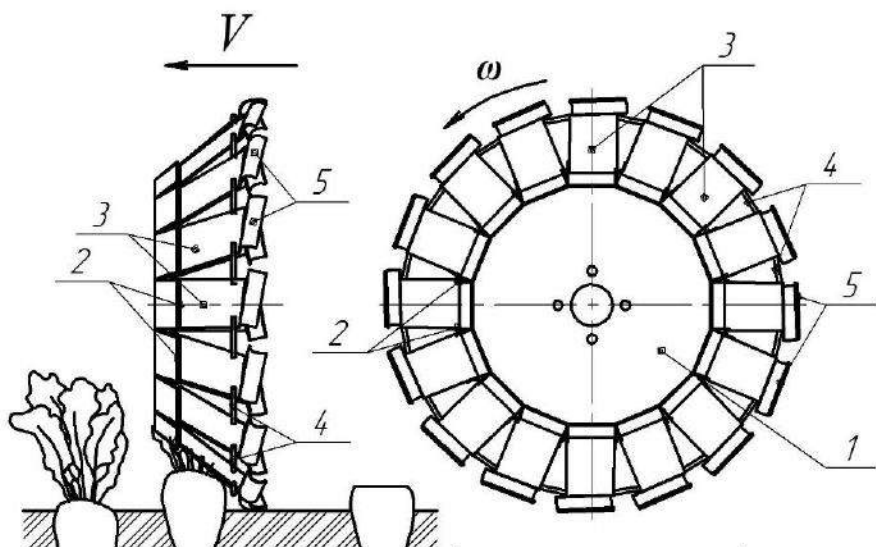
Конструкційна схема копірно-роторного гичковідокремлювача
